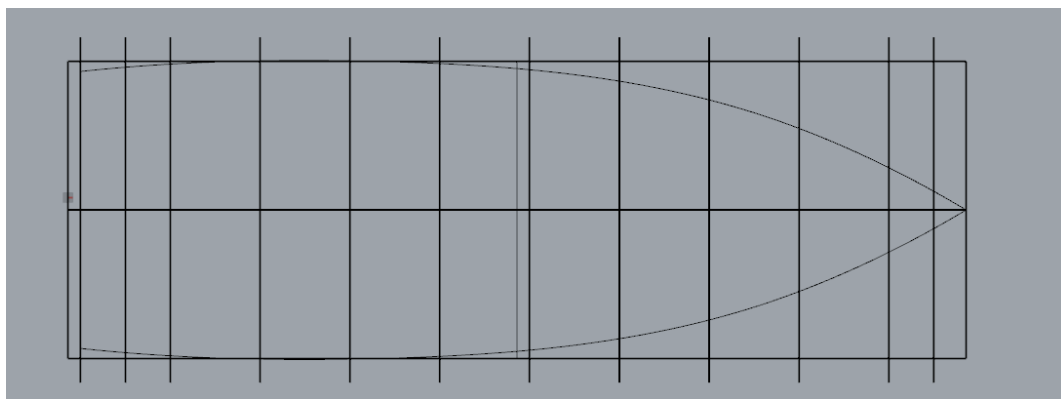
Vista en alzado de las secciones originales del velero. Editado con Rhinoceros
